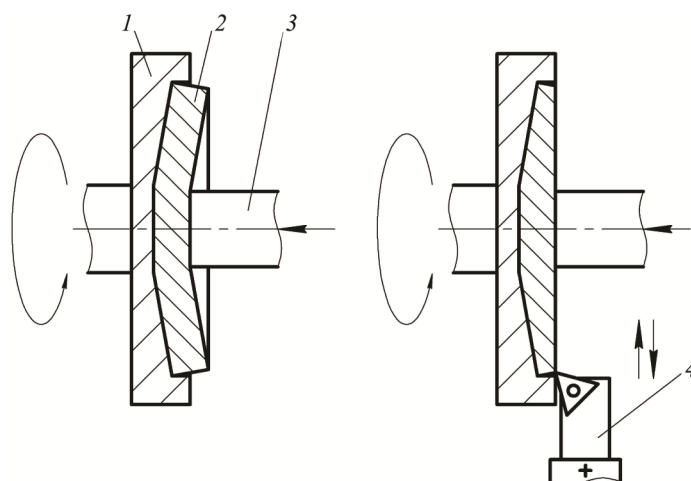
Схема получения дисковой заготовки переменной толщины:
